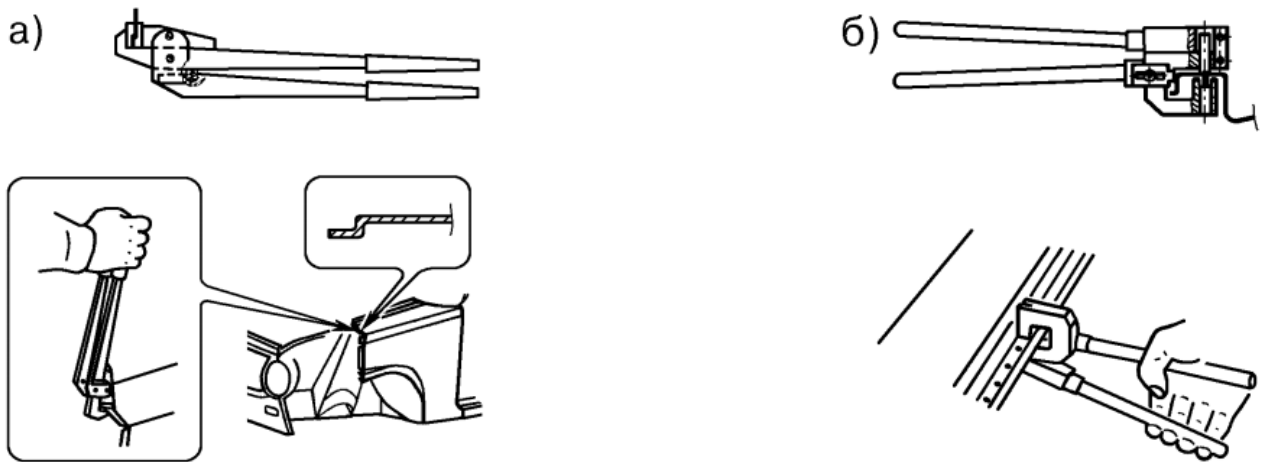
Технологічне обладнання для зварювання деталей кузова
